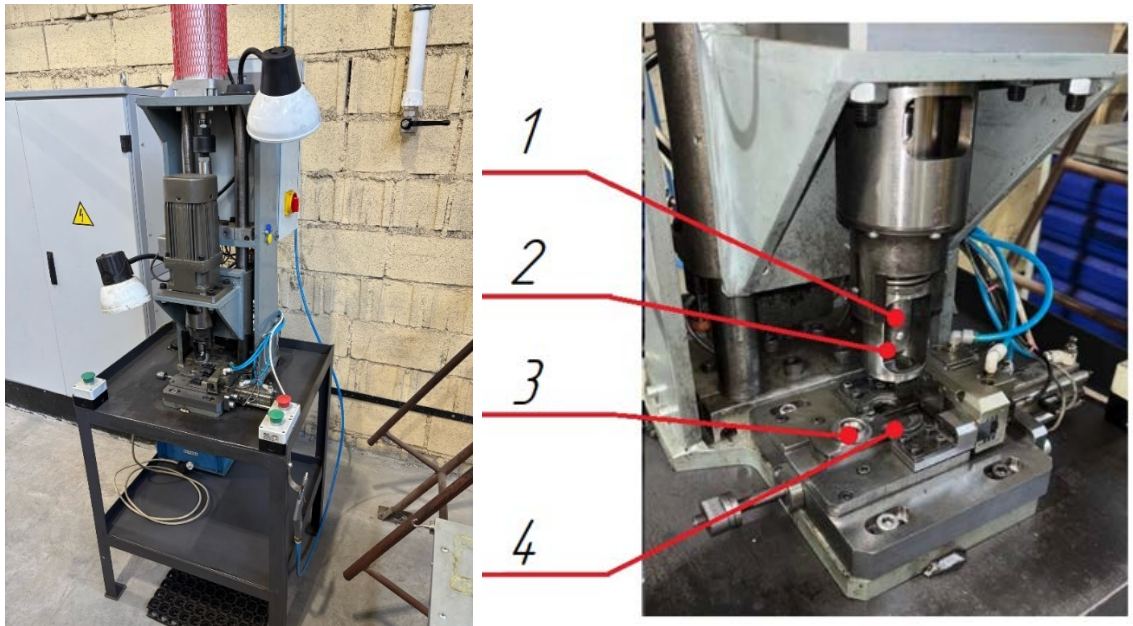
Внешний вид станка для раскатки отсекаателя: 1 – корпус раскатника; 2 – ролик; 3 – отсекаатель; 4 – опорные губки
